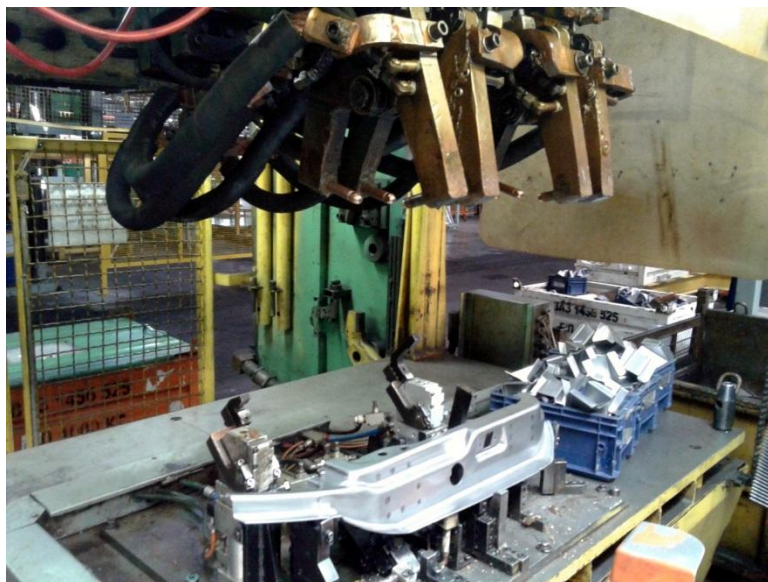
Контактная точечная сварка на многоэлектродной сварочной машине
